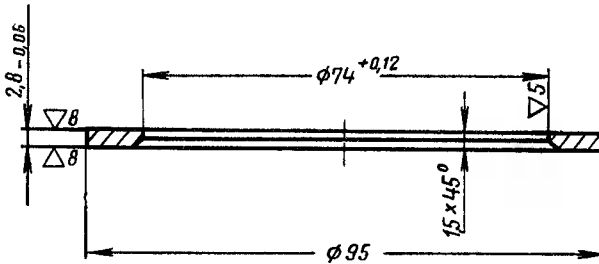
Опорная шайба шестерен нижней и верхней передач промежуточного вала раздаточной коробки (214Б-1802169)
